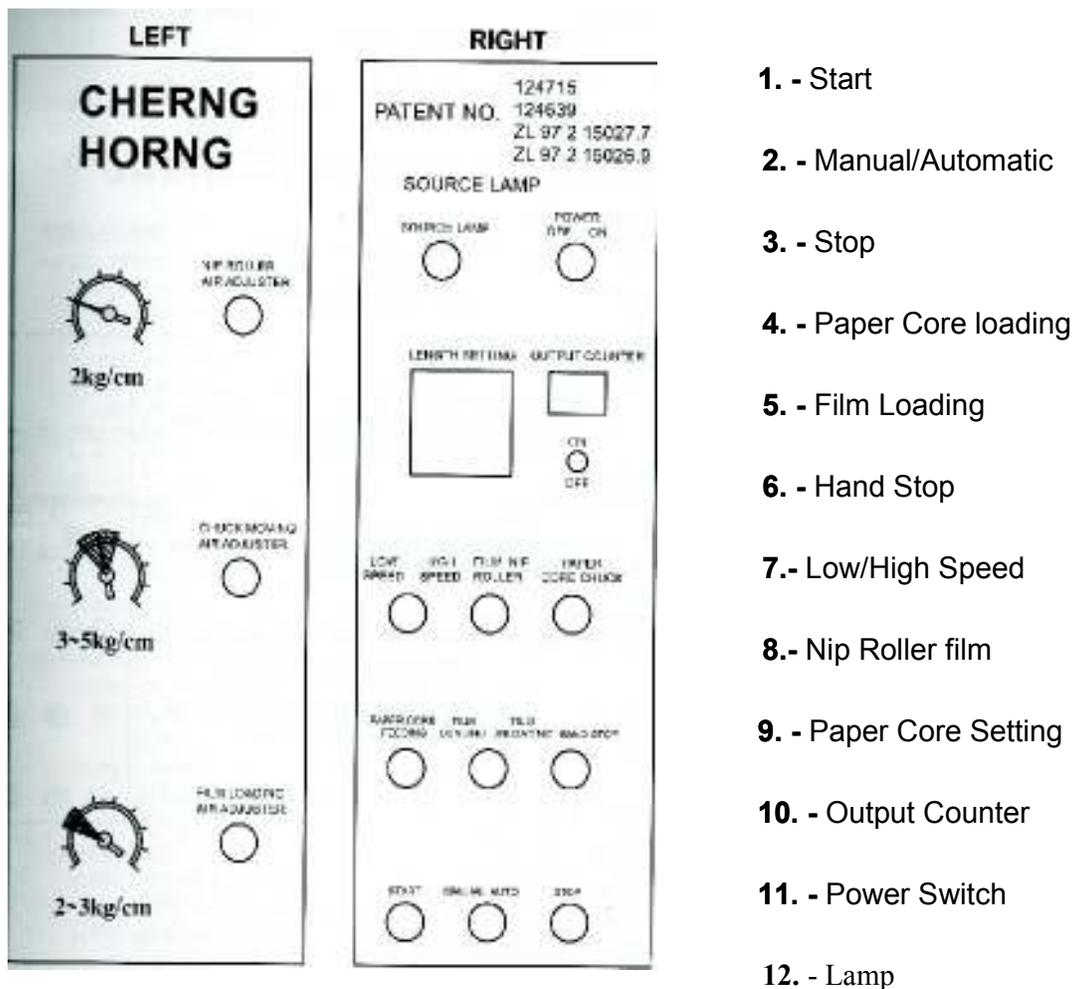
Máquina rebobinadora de lámina plástica stretch film
